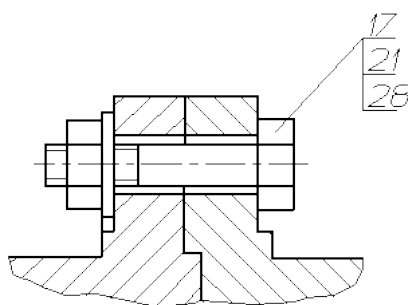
Пример группы крепежных деталей на сборочном чертеже
